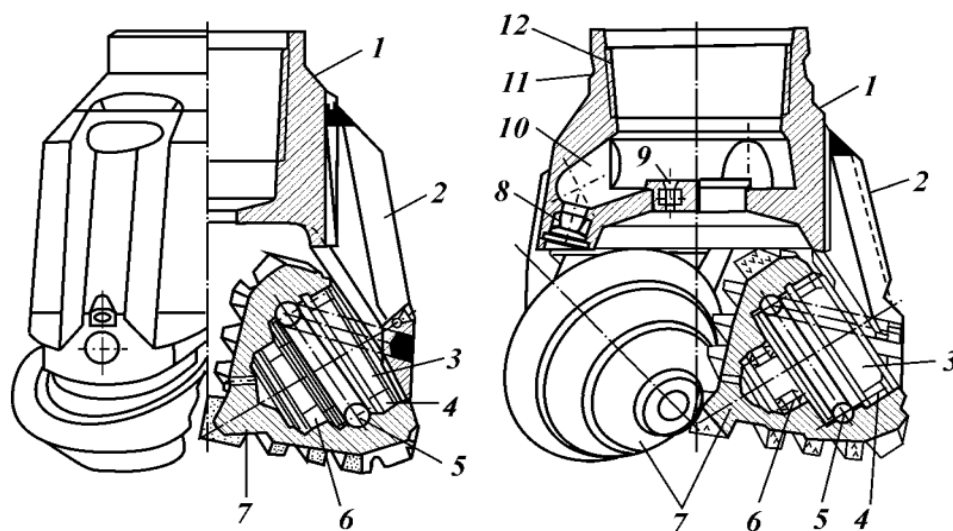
Конструкция наплавки путем газопламенного напыления с одновременным проплавлением
